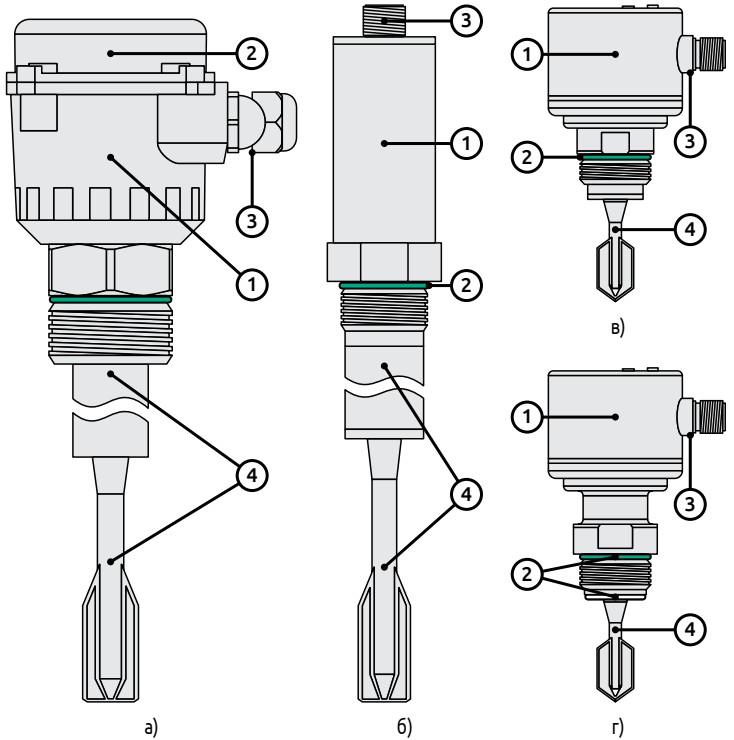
Внешний вид и назначение элементов конструкции:
